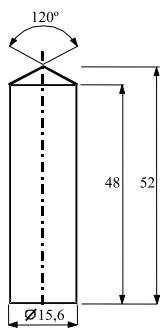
Piston cylindrique en bronze, dimensions en mm
